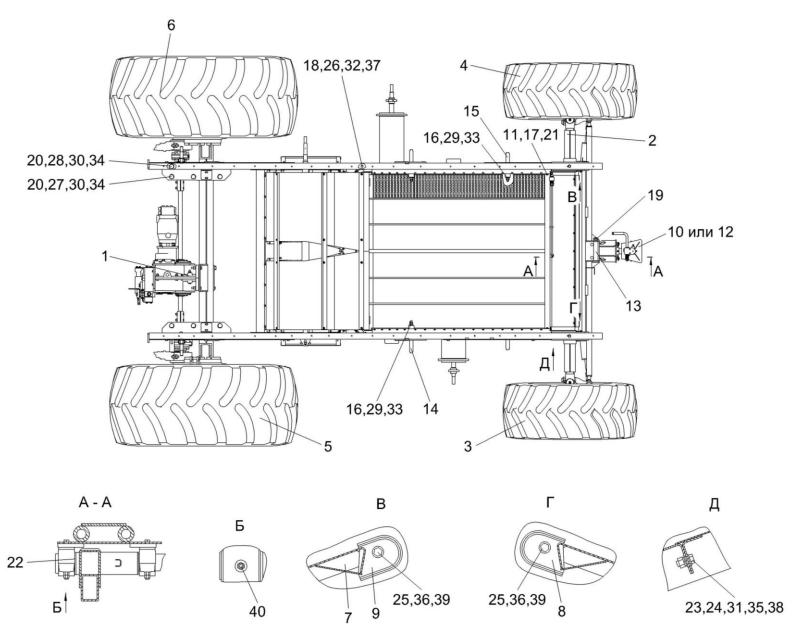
Шасси КЗК-10-0111010Р2 (вид сверху)
